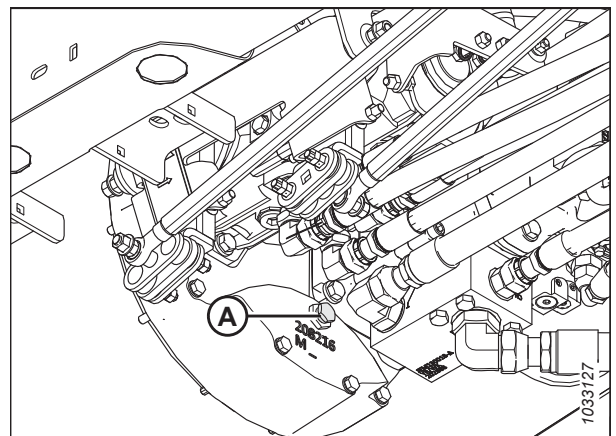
Getriebeschmiermittel-Kontrollschraube
